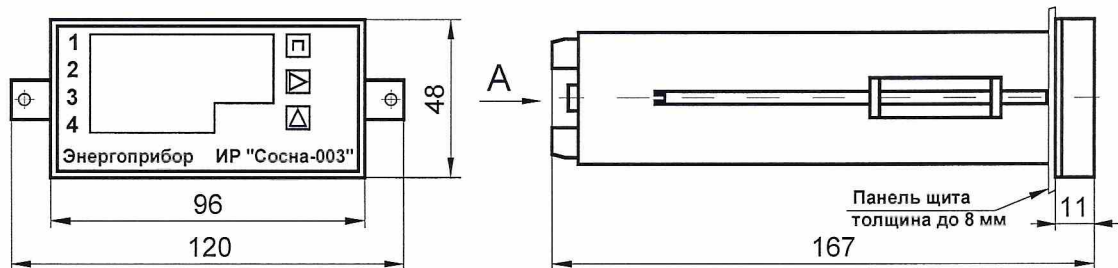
Габаритные и установочные размеры ИР "Сосна-002"
